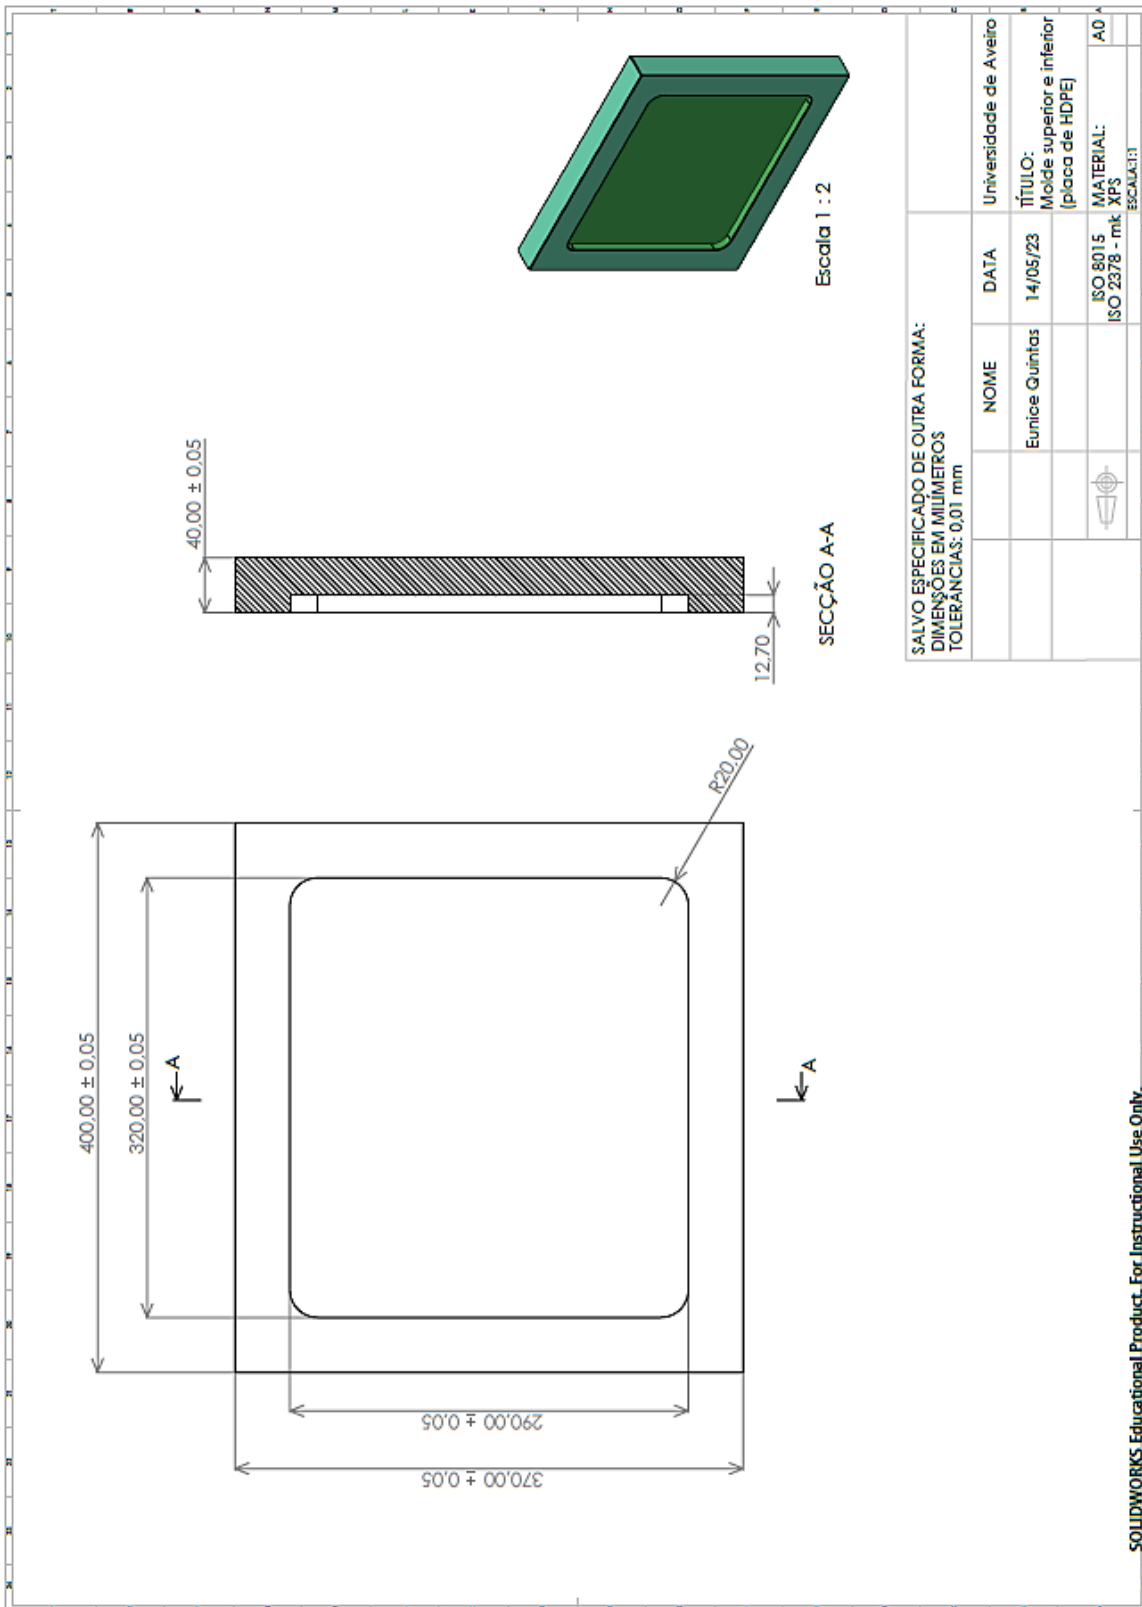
Desenho técnico do molde superior/inferior de XPS para a placa de HDPE.
